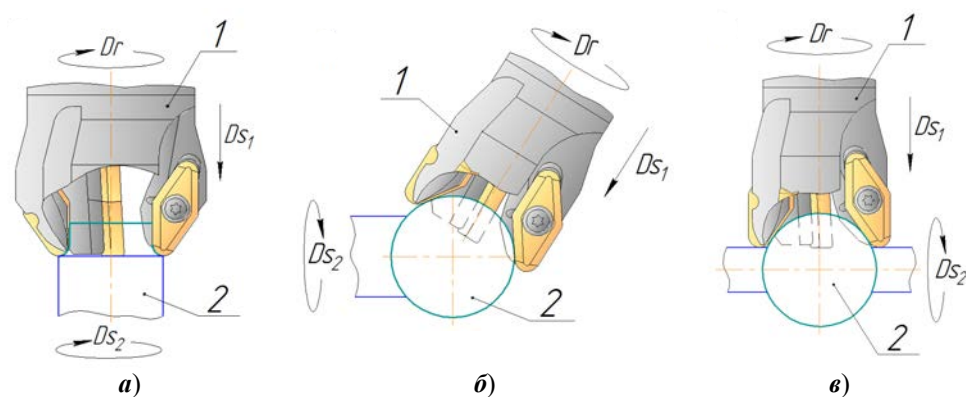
Схемы обработки охватывающими фрезами (зенкерами) поверхностей:
